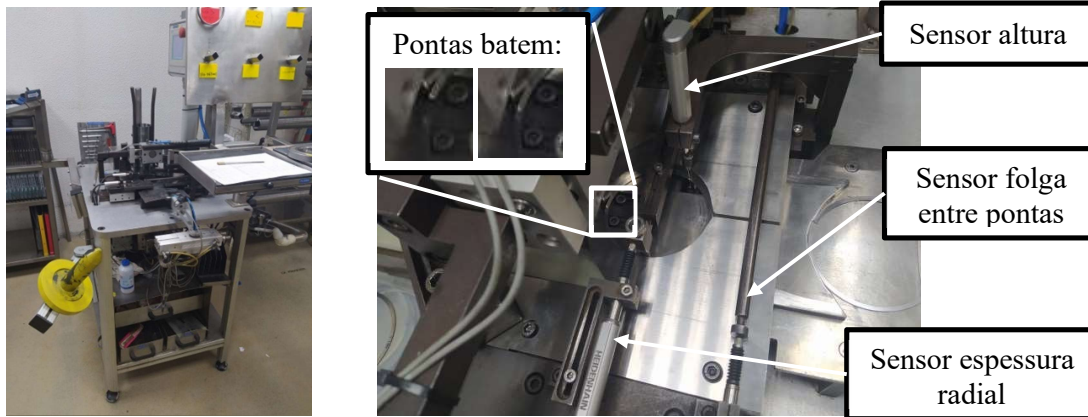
IPL - Máquina de Inspeção Linear - IPL
